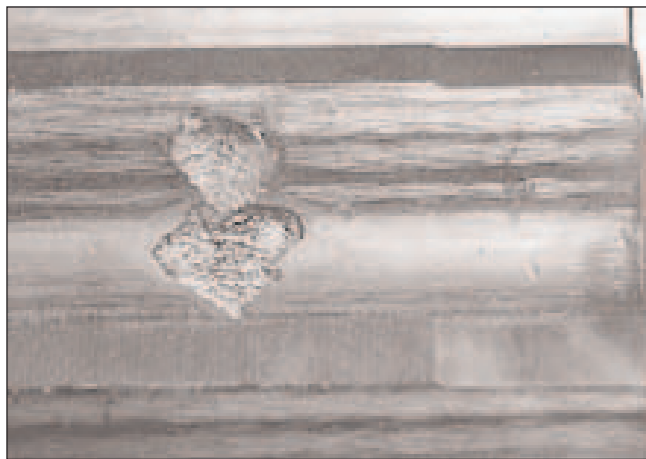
Dreieckiger Flankenausbruch nach 60.000 Bh / Triangular flank break-out after 60,000 h of operation
